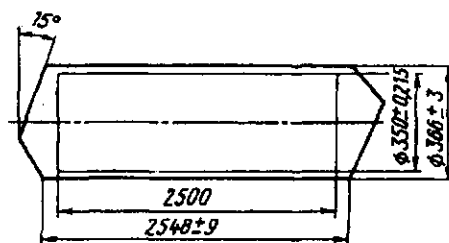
Рабочий чертеж вала, изготовляемого ковкой на прессе
